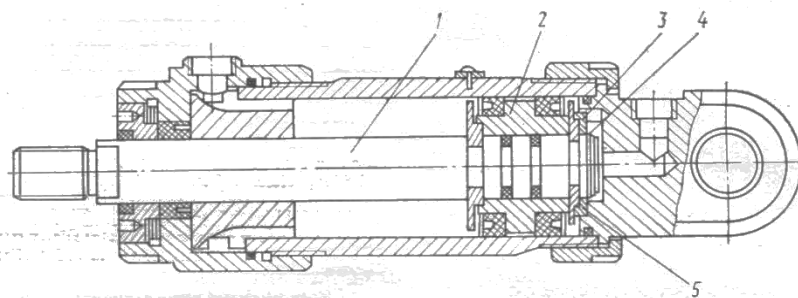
Гидроцилиндр с креплением крышек к гильзе на наружной резьбе
